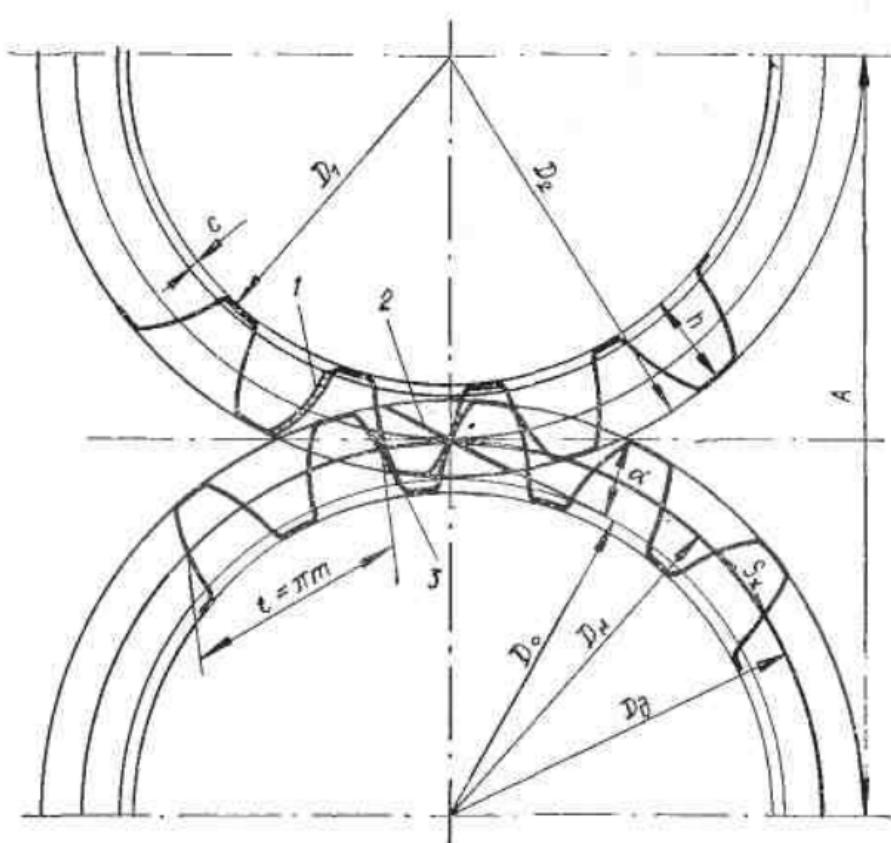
Основные элементы эвольвентного зубчатого зацепления:
